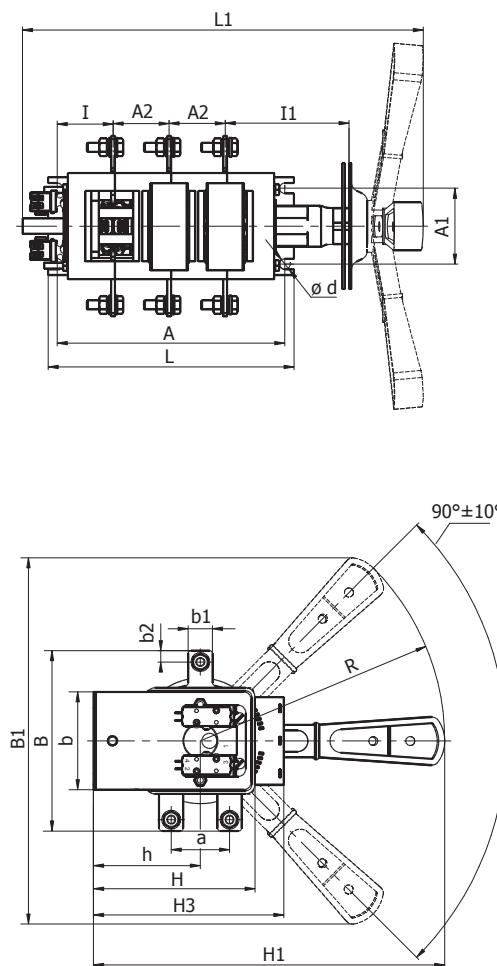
Выключатель-разъединитель трехполюсный на два направления с боковой смещенной рукояткой.
